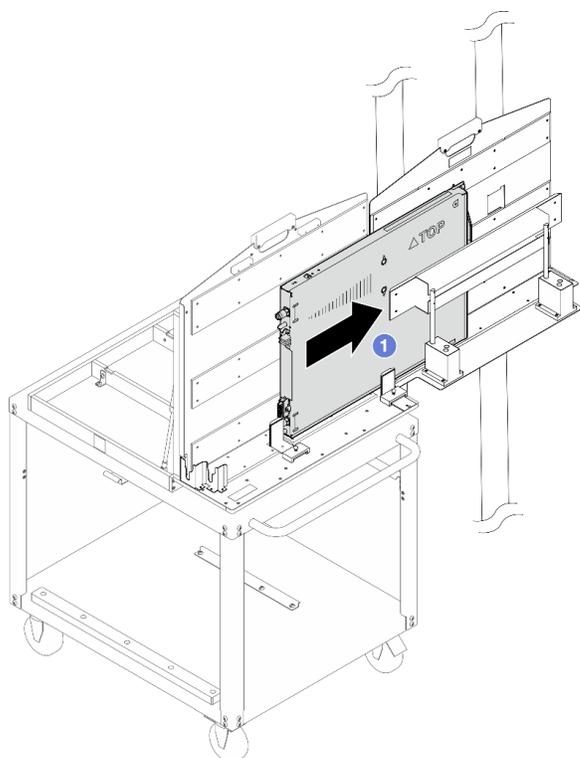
Transfert du plateau sur le dispositif d'outil de levage
